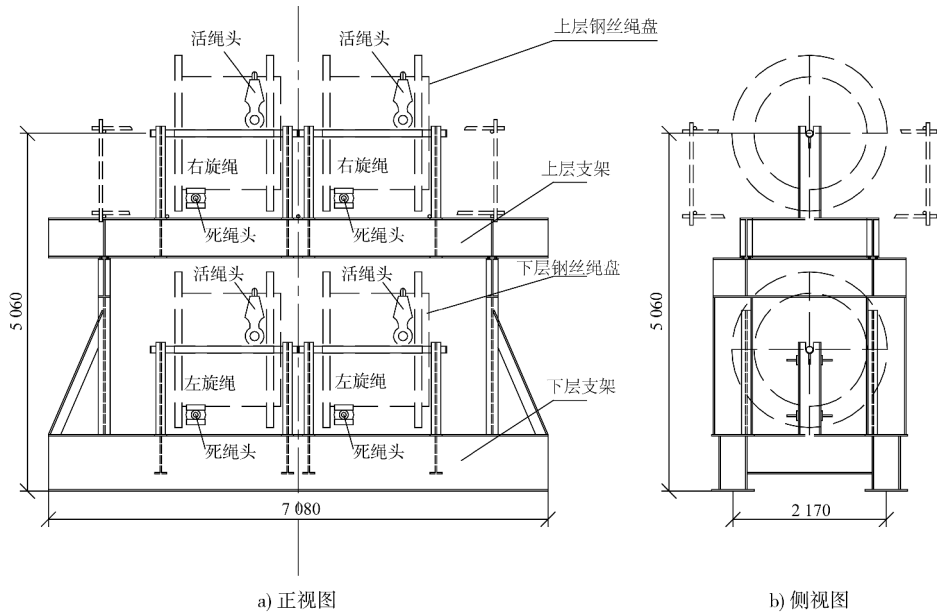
钢丝绳安装工装及钢丝绳布置 (单位: mm)
